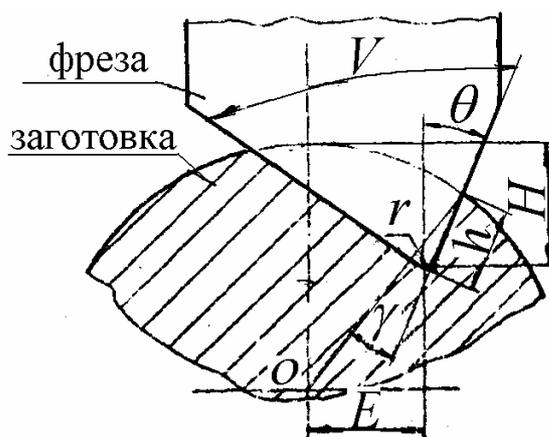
Установка рабочей фрезы для фрезерования канавки
